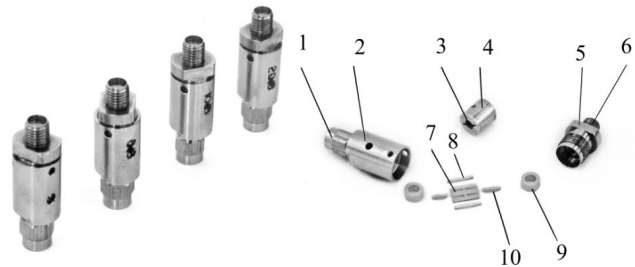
Внешний вид и узлы аттенюатора в коаксиальном тракте сечением 3,5/1,52 мм: 1, 6 – высокочастотные разъемы корпуса аттенюатора; 2, 5 – свинчивающиеся части корпуса аттенюатора; 3 – продольный паз, в который вставляется пластинчатый резистор 7 с пружинными контактами 8; 4 – втулка, внутренний диаметр которой равен 3,5 мм; 9 – удлинительное кольцо; 10 – электрод, надеваемый на центральный проводник резистора
